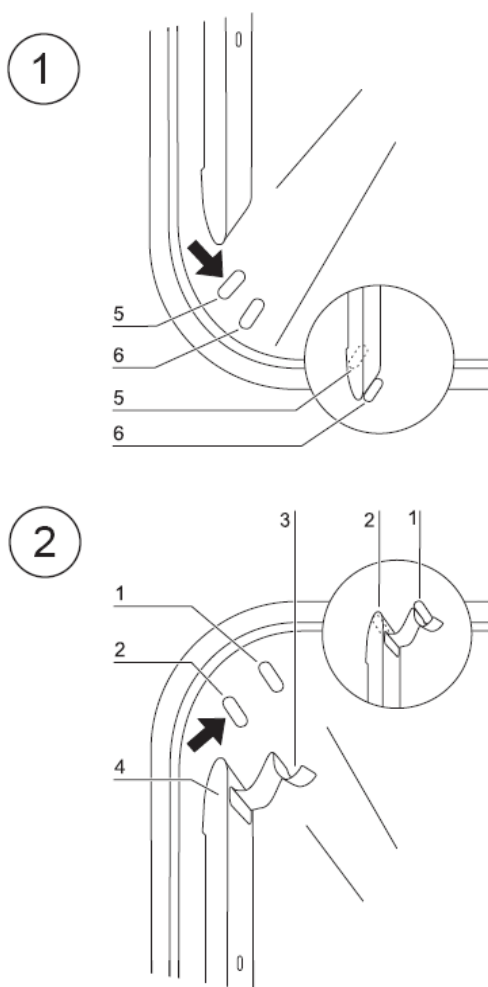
Монтаж и демонтаж креплений и полок
